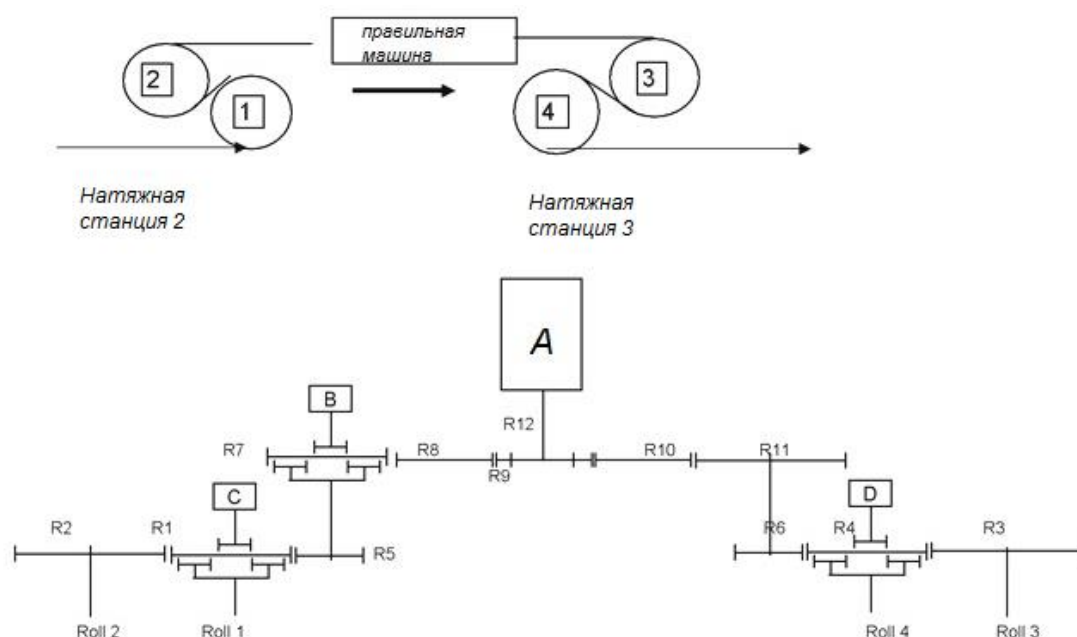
Схема расположения зубчатых колес редукторов ИРМ: А – двигатель главного привода; В – двигатель привода удлинения; С – двигатель НС №2; D – двигатель НС №3; 1 – ролик, связанный через планетарный редуктор с двигателем С; 2 – ролик, который расположен на входе в ИРМ; 3 – ролик, расположенный на выходе из ИРМ; 4 – ролик, связанный через планетарный редуктор с двигателем D
